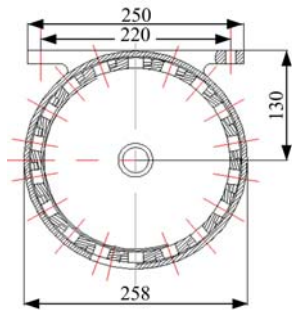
组合内窝孔精密排种器的 CAD 模型(主视图)
